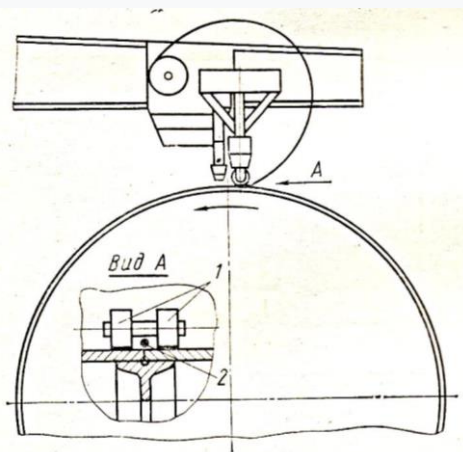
Схема автоматичного зварювання кільцевого шва з використанням пристосування для притискання кромок до підкладного кільця:
